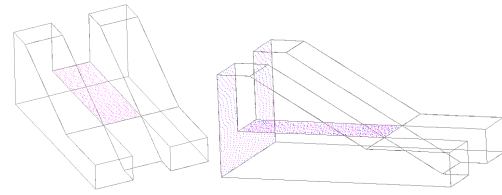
Sous-ensembles de points 3D utilisés pour le contrôle des tolérances géométriques
